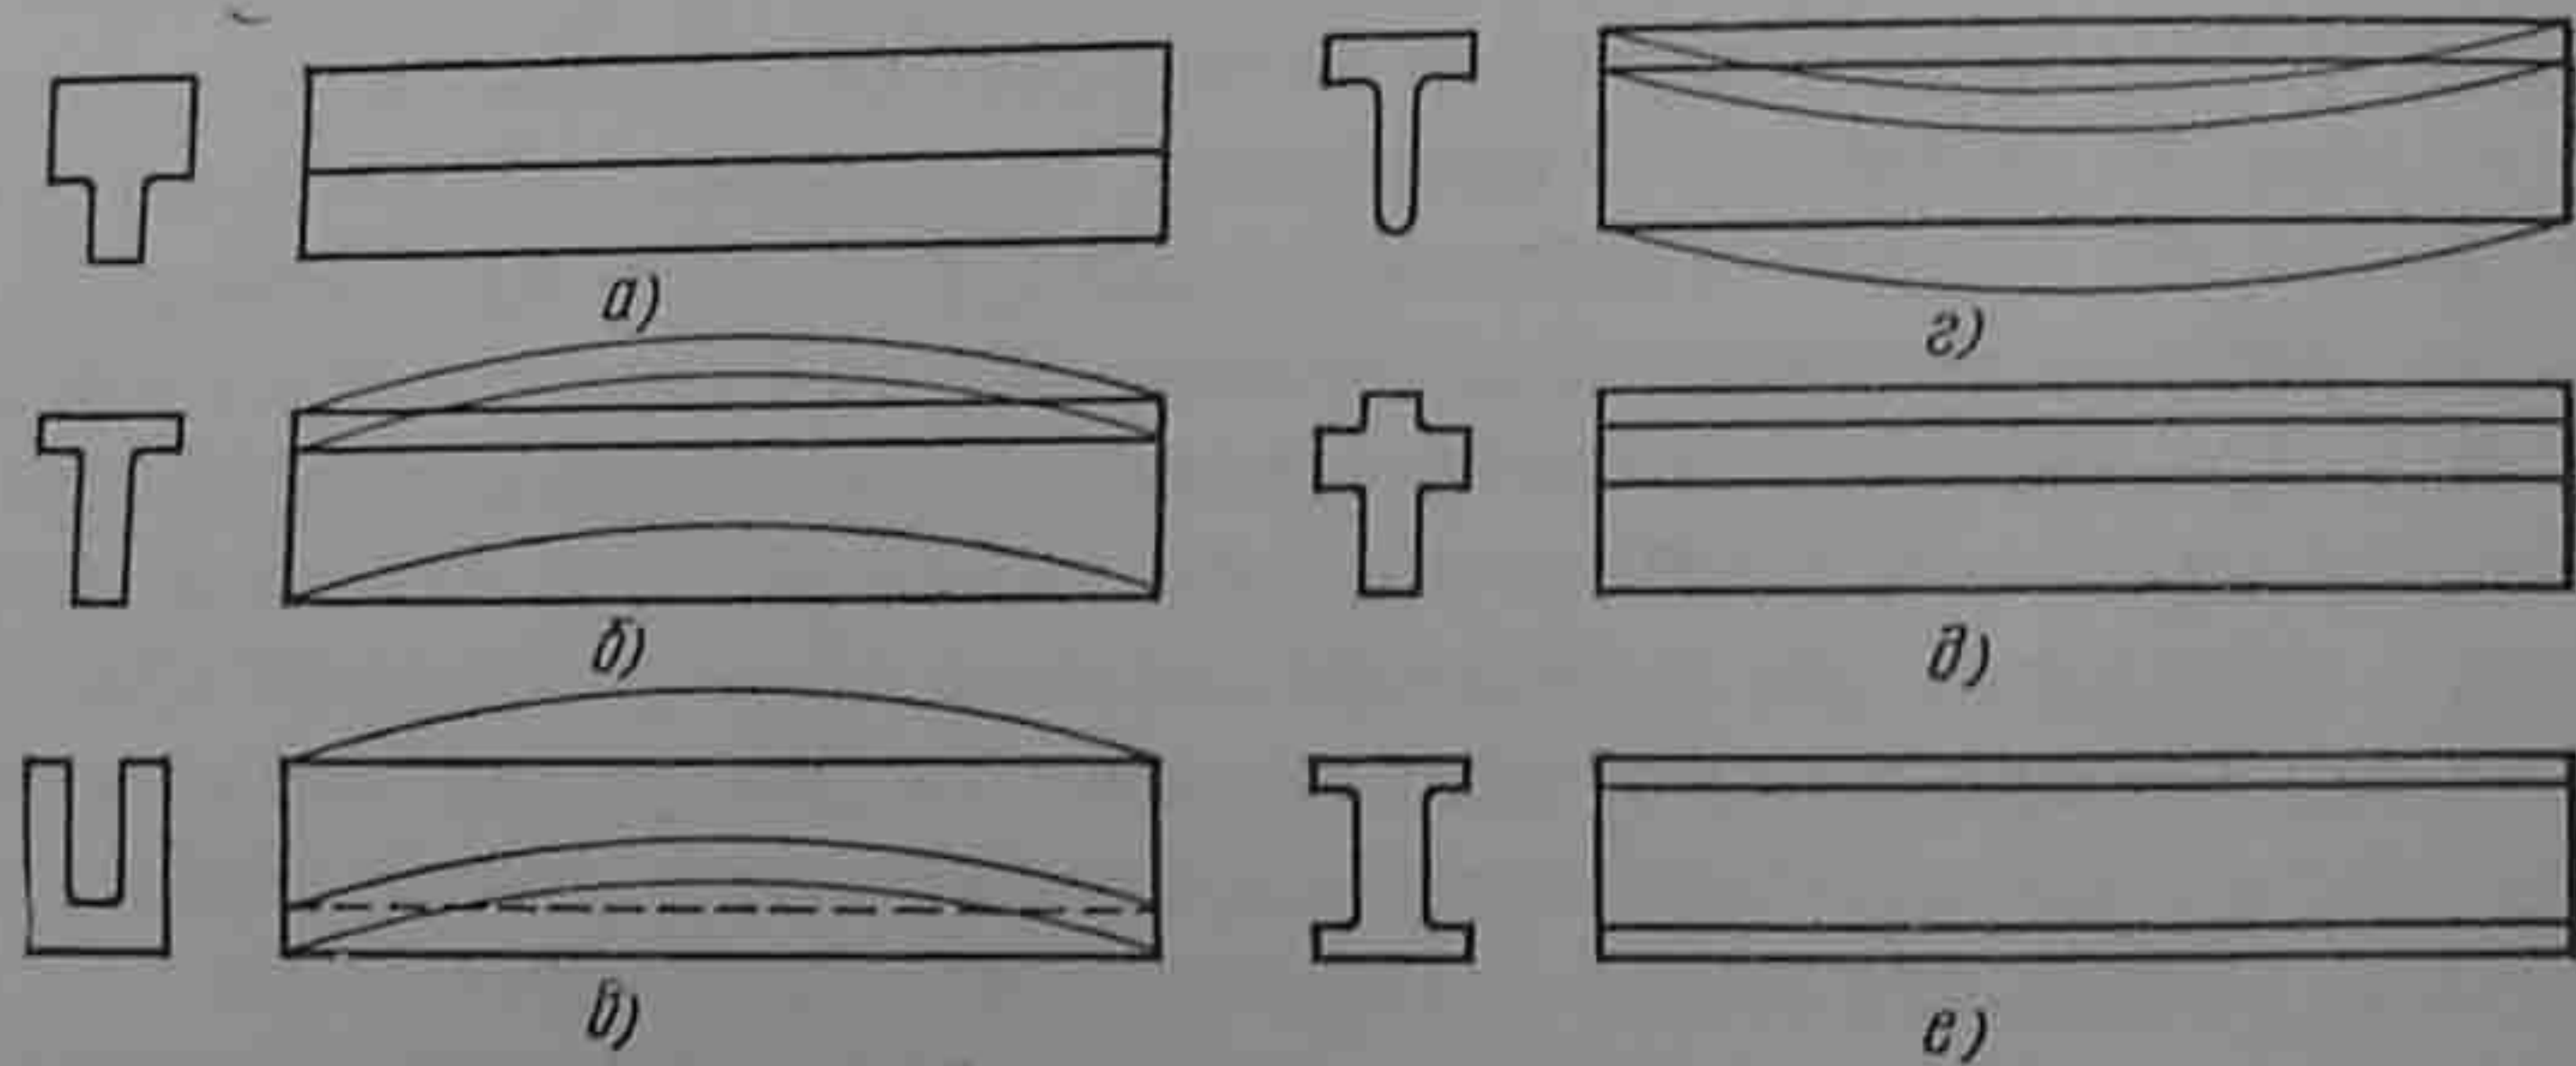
Влияние конструкции профиля бруска на характер его коробления (коробление отливки показано тонкой линией)
